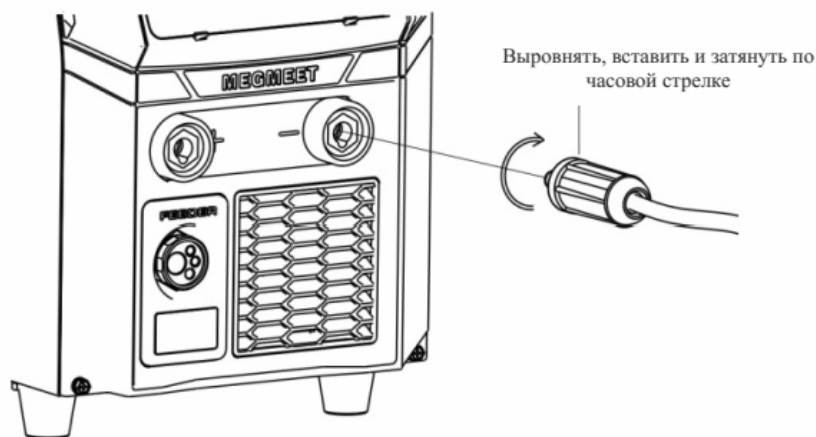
Схема подключения обратного сварочного кабеля ("земля") к заготовке
